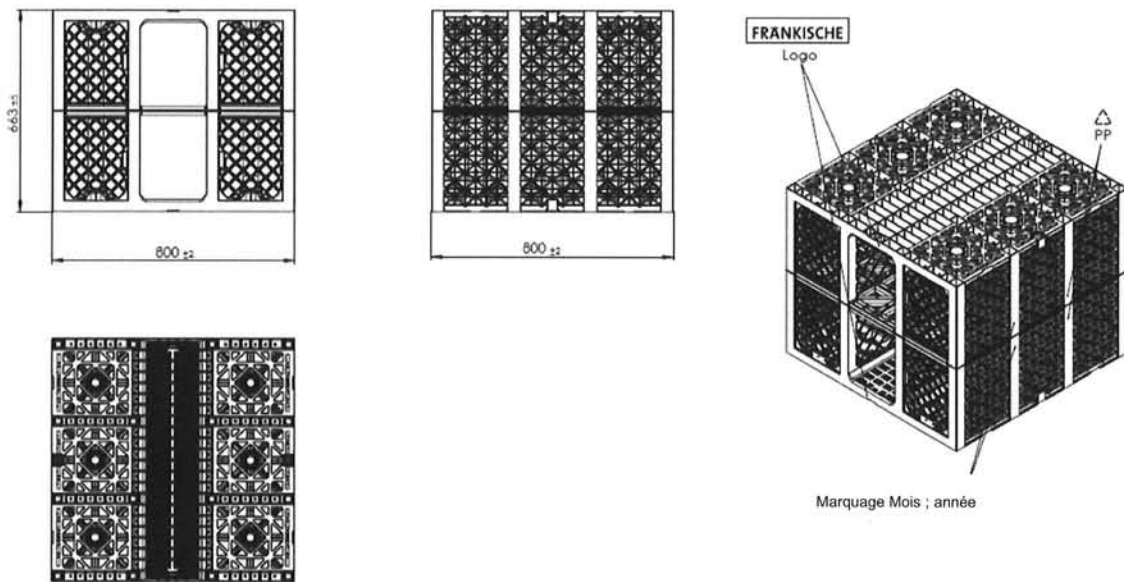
b- Caractéristiques dimensionnelles du module RIGOFILL INSPECT
